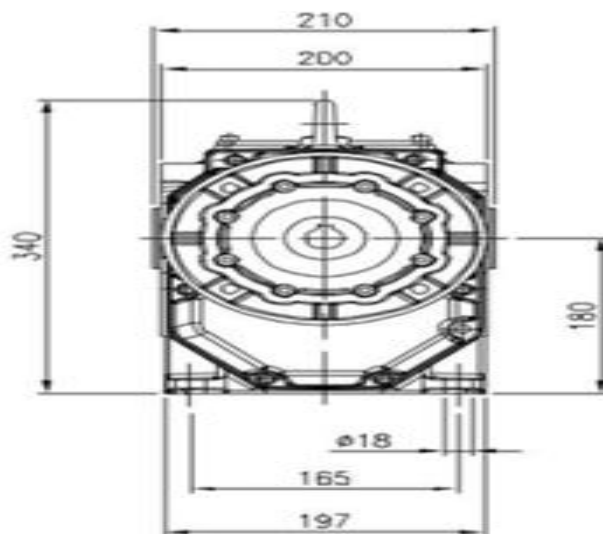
REDUCTEUR DIMENSION 210 MM
